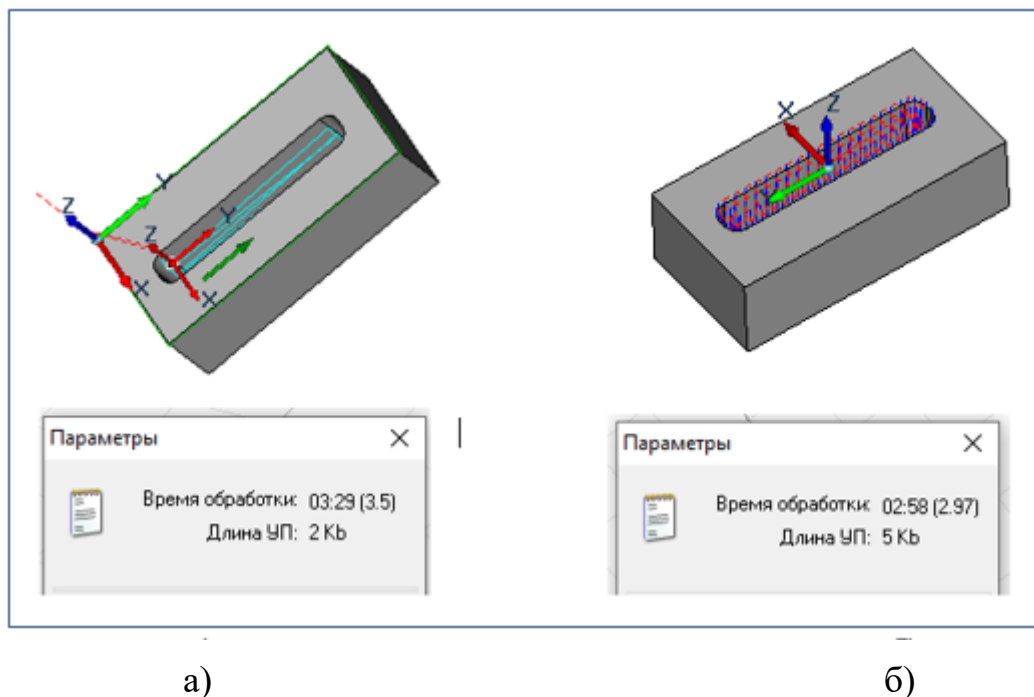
Траектории перемещения фрезы и расчетные параметры обработки: а - контурное фрезерование; б - плунжерное фрезерование
